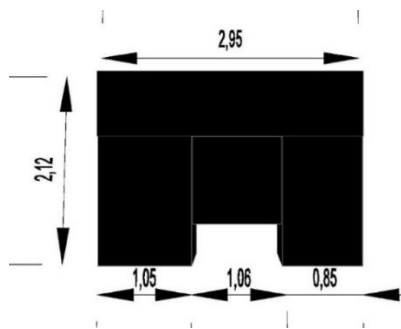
Dimensiones del sensor Sharp visto desde la parte superior
